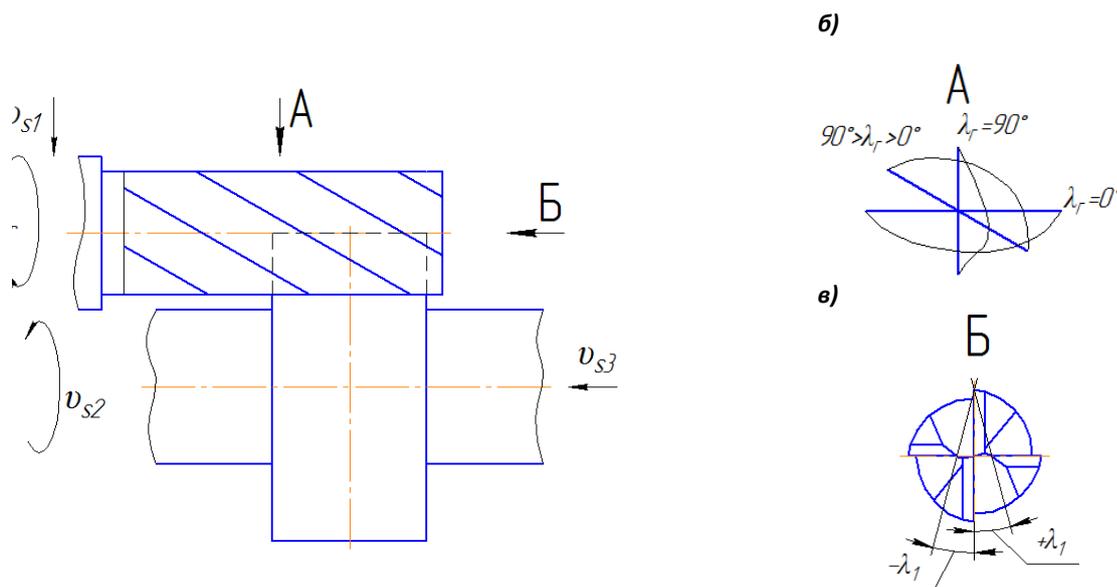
Схема обработки плоской поверхности вращающейся детали вращающимся инструментом (а) и возможные углы наклона режущей кромки на цилиндрической (б) и торцевой (в) поверхностях концевой фрезы
